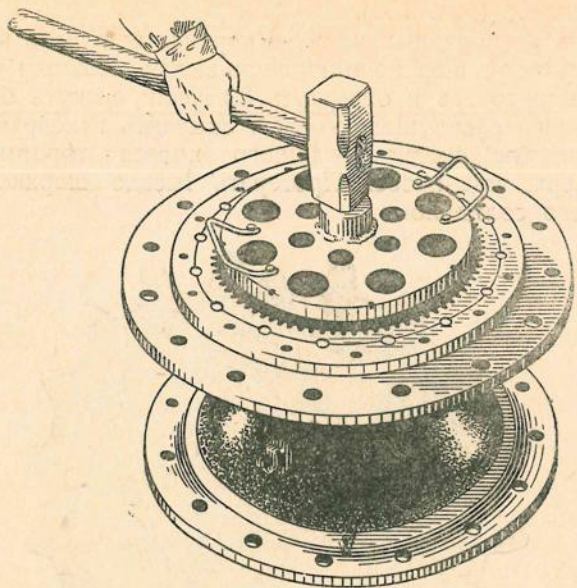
Запрессовка шарикоподшипника в корпус ведущего колеса при помощи оправки
